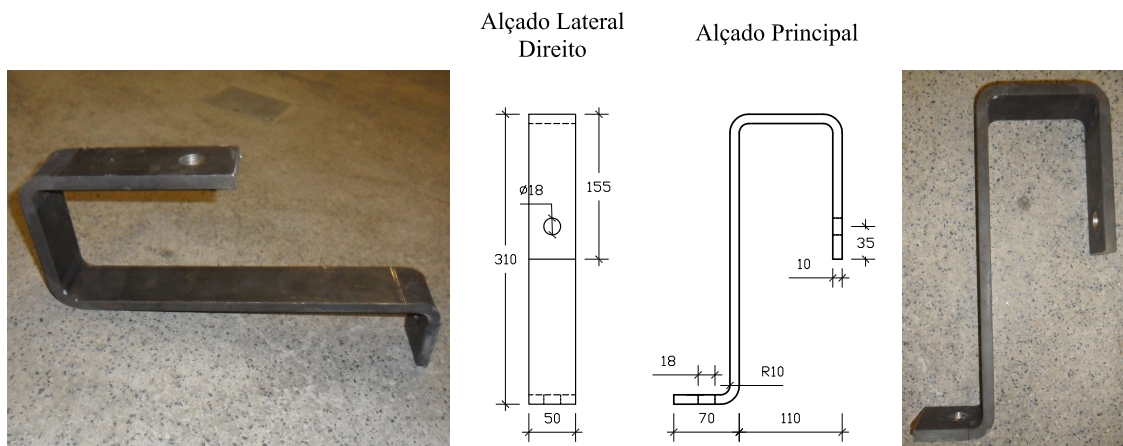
Vistas e dimensões do dispositivo DR 50x10-1 (mm)
